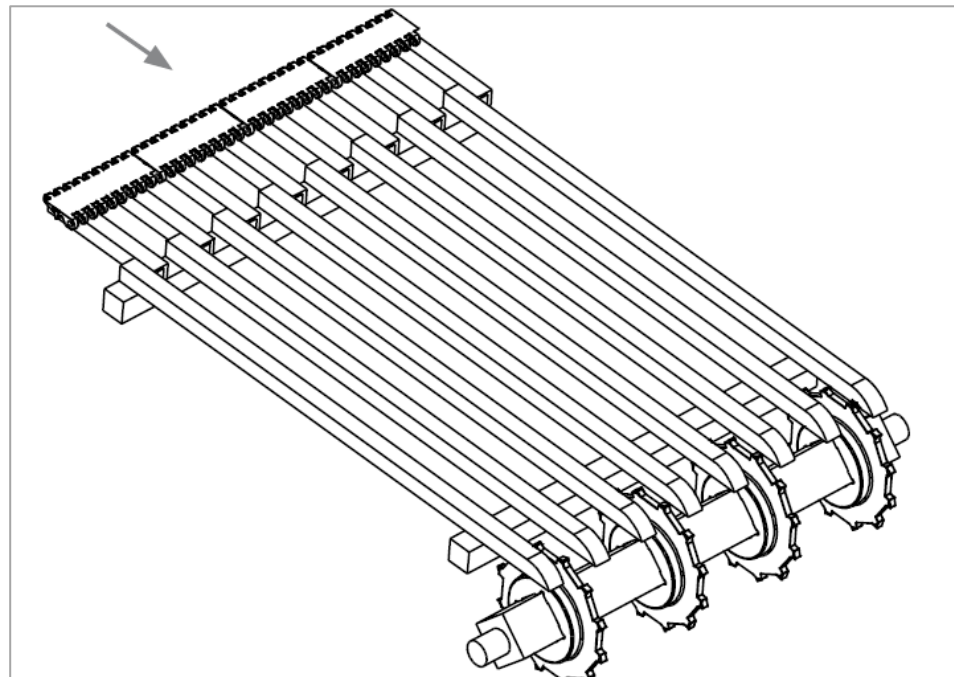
Disposición de engranajes. [Ammeraal Beltech]
